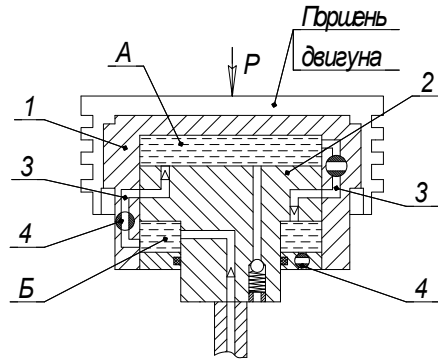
Схема механізму зміни ступеня стиску: А – верхня порожнина; Б – нижня порожнина
